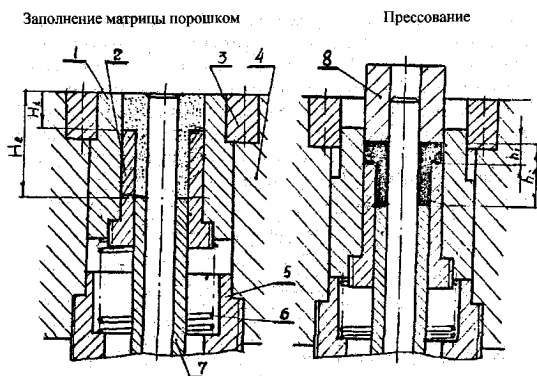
Схема пресс-формы для прессования втулок с наружным верхним буртом: 1 - матрица; 2, 7 - составные элементы нижнего пуансона; 3 - кольцо; 4 - обойма; 5 — упор; 6 - пружина; 8 - верхний пуансон
